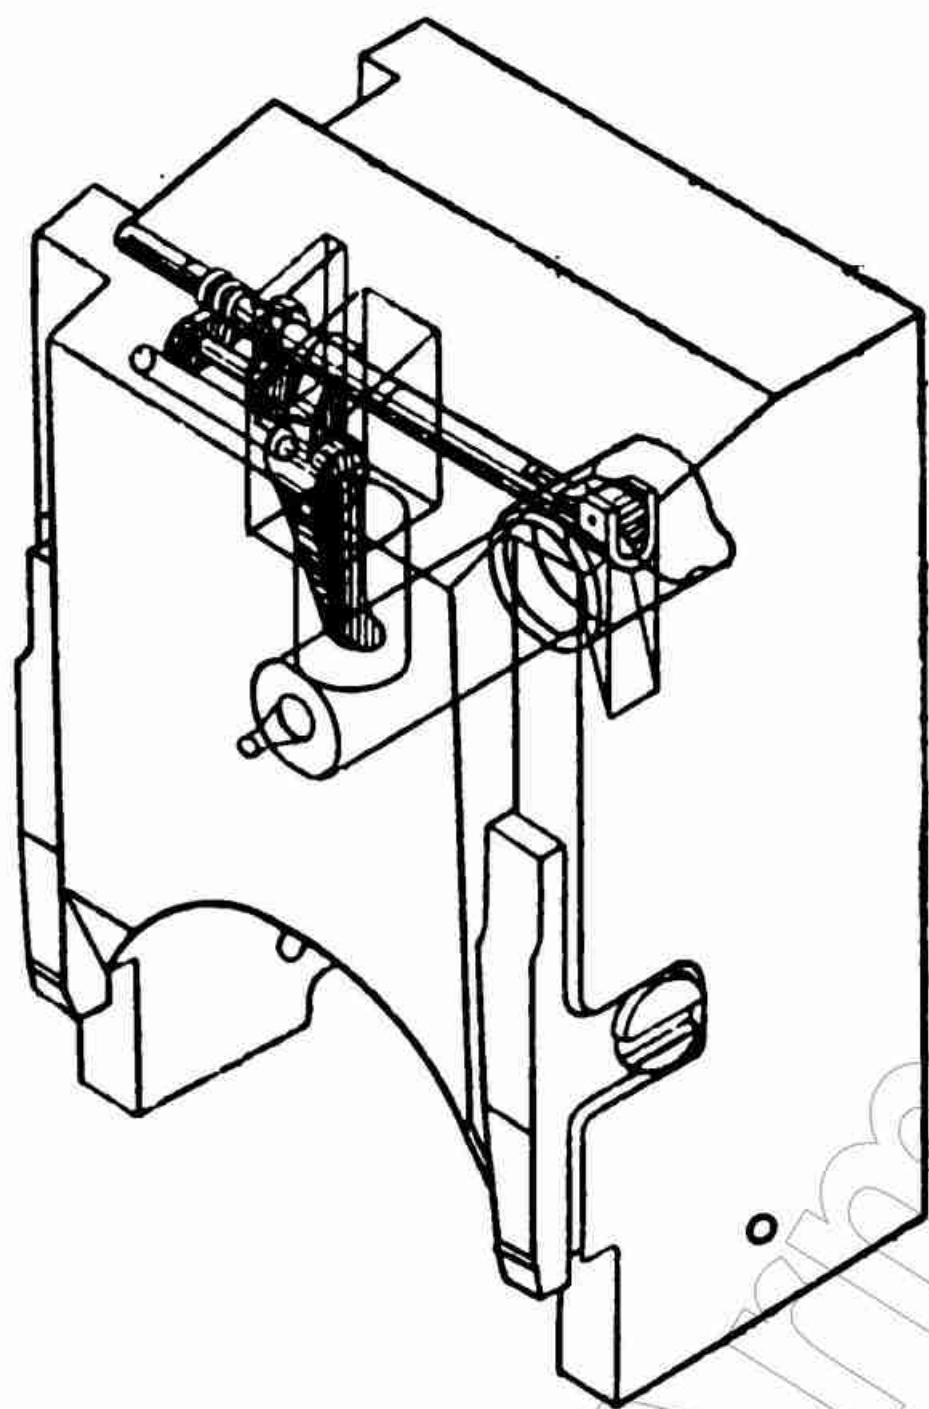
Положение деталей ударного и предохранительного механизмов при сборке (третья операция)
